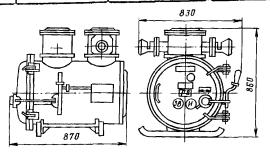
Габаритные размеры пускателя ПВИ-250БТ
